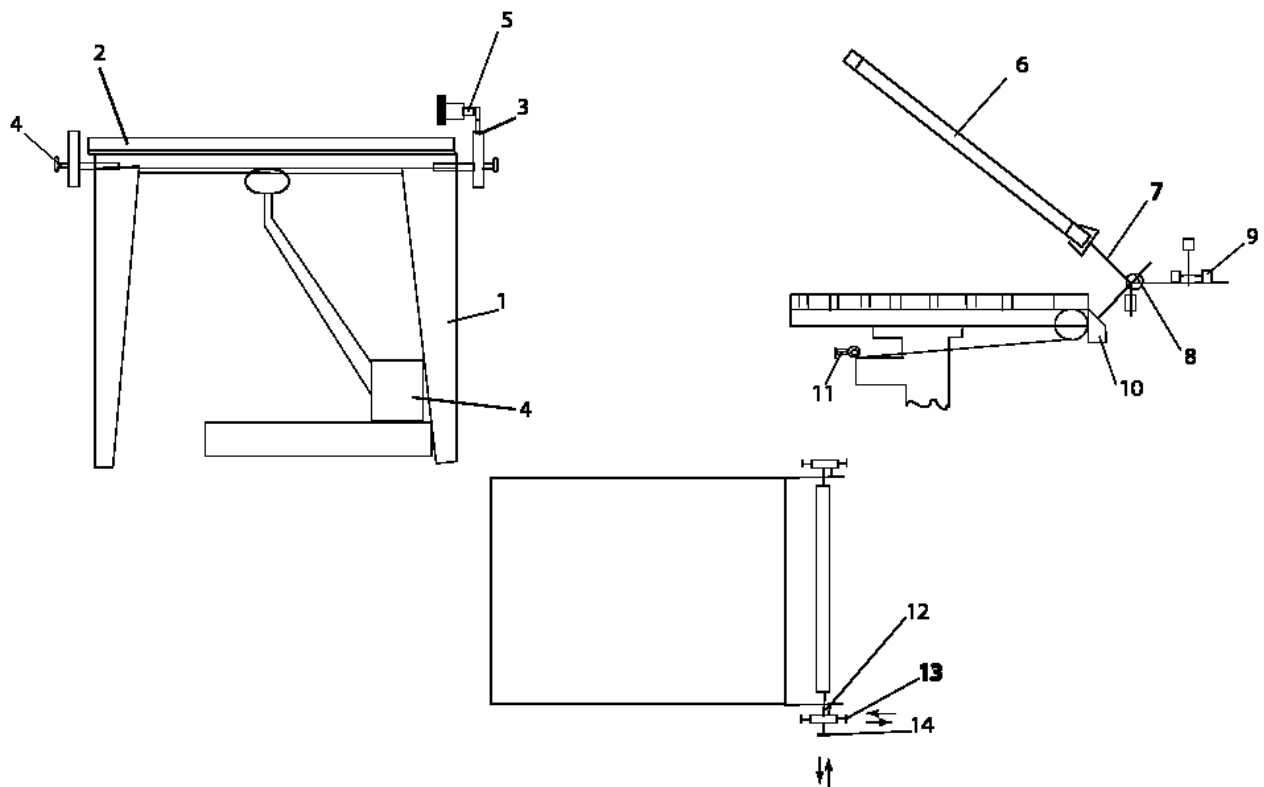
Схема верстату трафаретного друку: 1 – каркас; 2 – друкарський стіл; 3, 4 – регулятори висоти форми; 5, 12 – фіксуючі гвинти; 6 – форма; 7 – формотримувач; 8 – вал; 9 – противаги форми; 10 – упор; 11 – зсув; 13, 14 – регулюючі гвинти для здійснення приводки.
